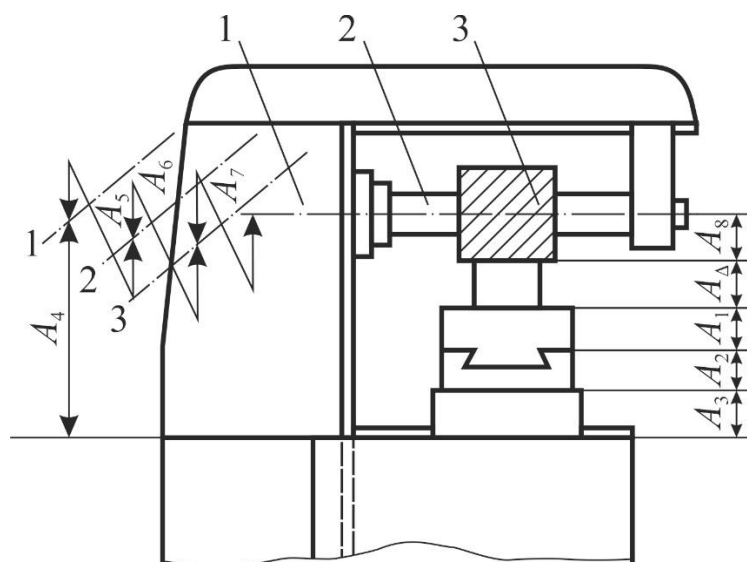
Размерная цепь технологической системы (технологического перехода универсально-фрезерного станка): 1, 2, 3 – соответственно оси шпинделя станка, оправки и фрезы
